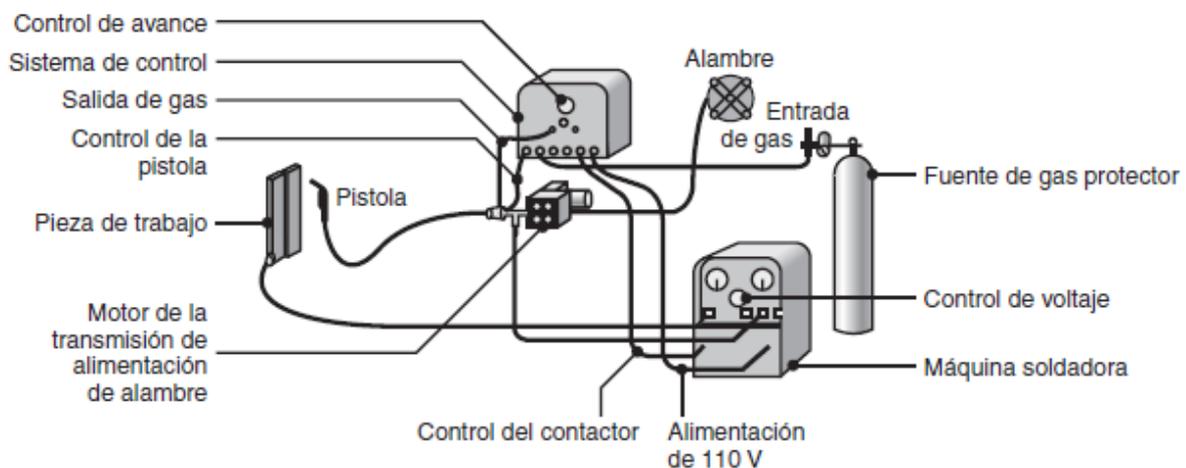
Equipo básico para soldadura GMAW (Fuente: *Manufactura, Ingeniería y Tecnología*)
